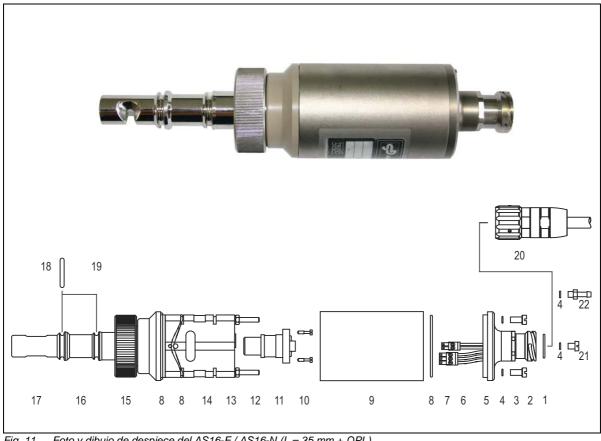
Foto y dibujo de despiece del AS16-F / AS16-N (L = 35 mm + OPL)
